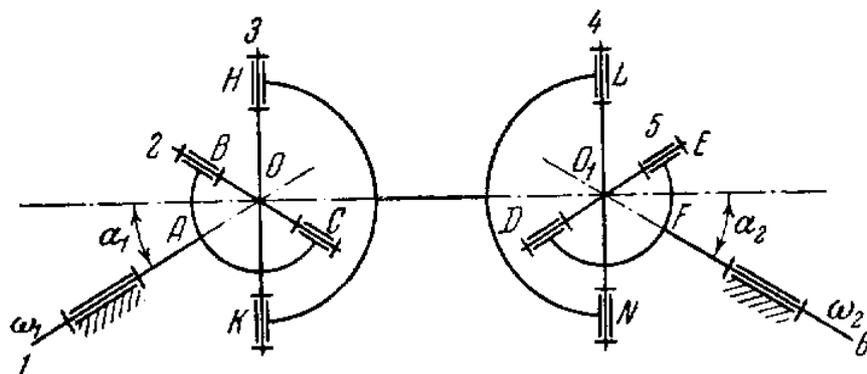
Кинематическая схема механизм двойного универсального шарнира
